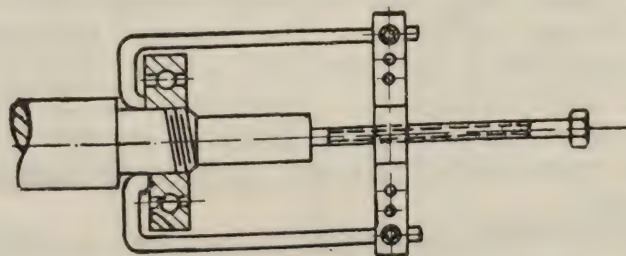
Приспособление для снятия колец роликовых и шариковых подшипников.
